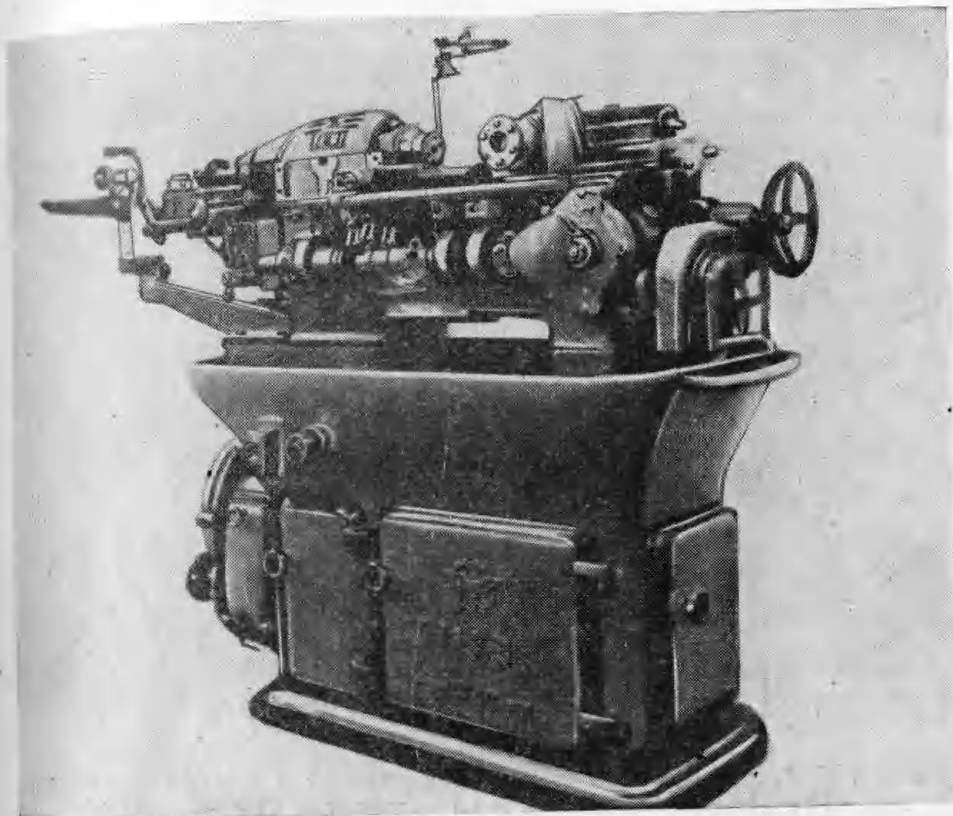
Токарно-револьверный универсальный станок с вертикальной головкой мод. 1А36. Диаметр прутка 63 мм (станкозавод имени Орджоникидзе).
